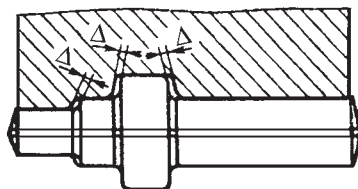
Зазор между неопорными поверхностями пуансона и поковки
